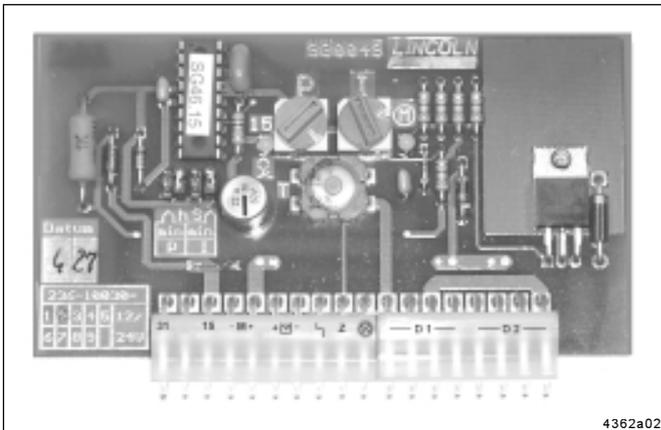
Steuerplatine 236-10030-1 gezeigt
